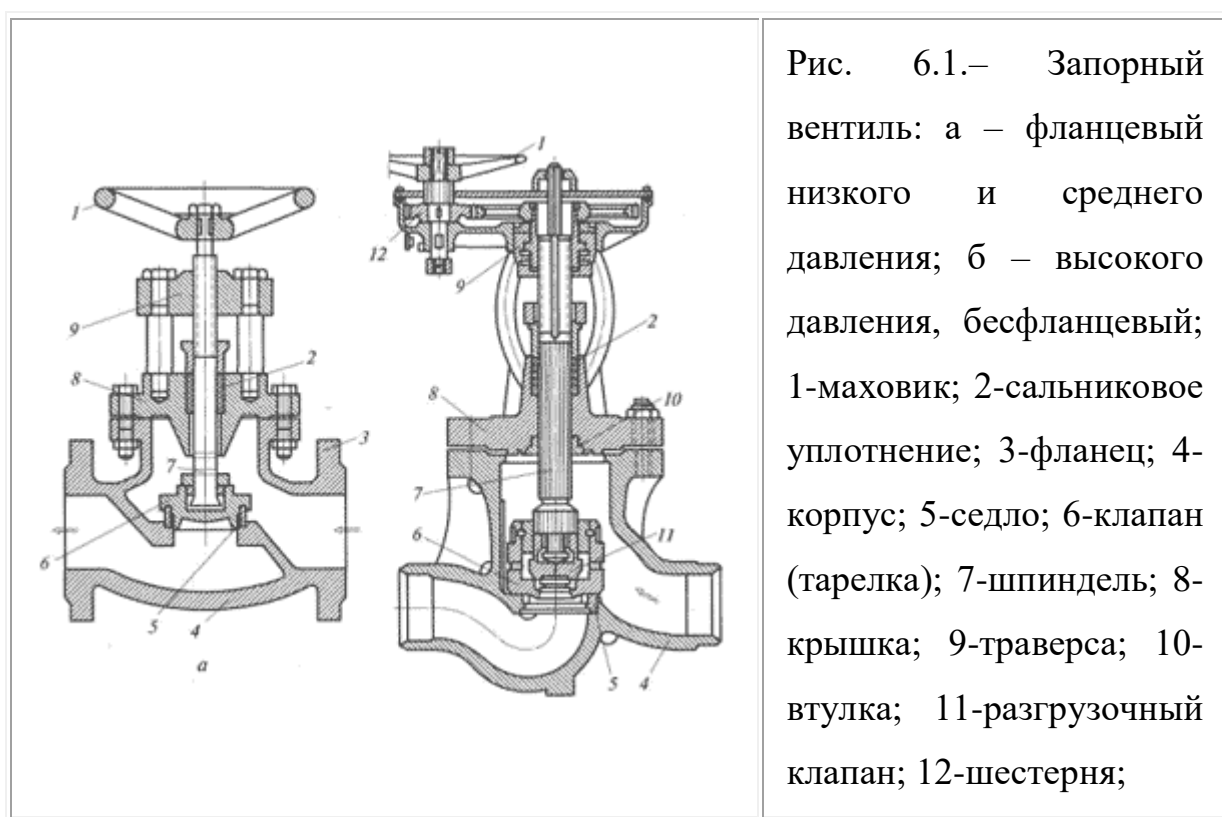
Запорный вентиль: а – фланцевый низкого и среднего давления; б – высокого давления, бесфланцевый; 1-маховик; 2-сальниковое уплотнение; 3-фланец; 4-корпус; 5-седло; 6-клапан (тарелка); 7-шпиндель; 8-крышка; 9-траверса; 10-штулка; 11-разгрузочный клапан; 12-шестерня;
